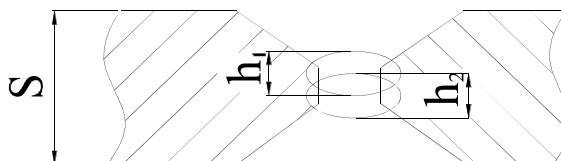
Первый проход при односторонней сварке.
